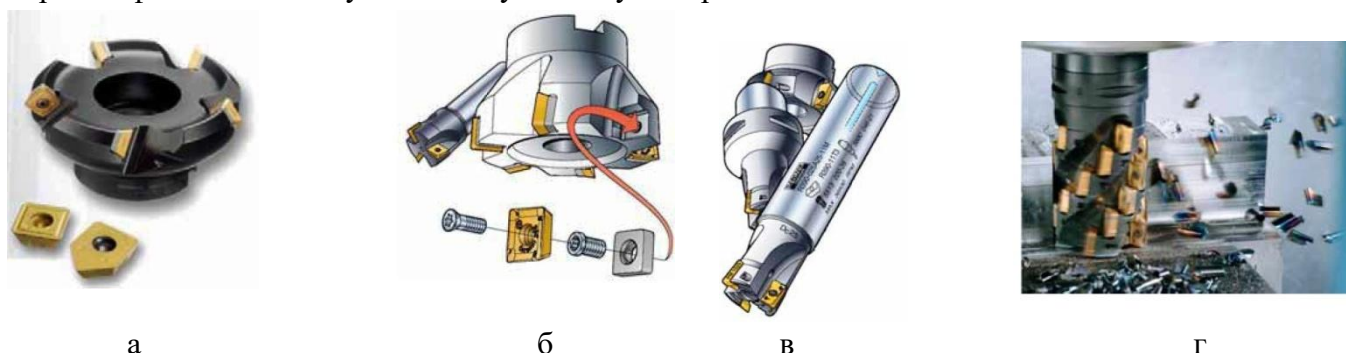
Фрези CoroMill 245 (а); CoroMill 290 (б); CoroMill 390 (в) і двокромочні (г)
